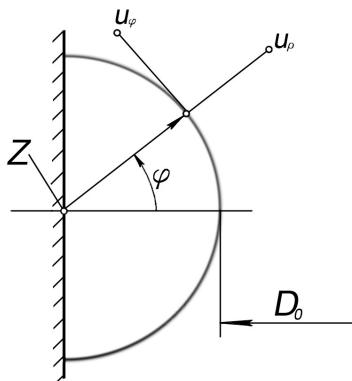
Розрахункова схема кільця давача магазину для гайок
